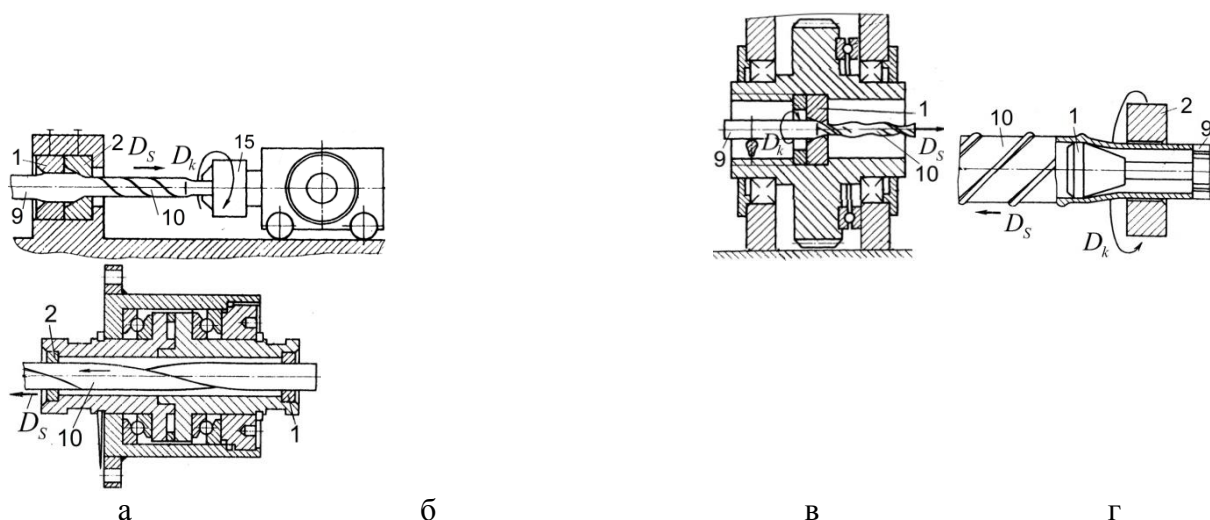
Типові технологічні способи формоутворення ГЗ і ШЗ: 1, 2 - інструменти (волока, голка, оправа); 9 – початкова заготовка, 10 – скручені ГЗ або ШЗ, 15 - захвати
